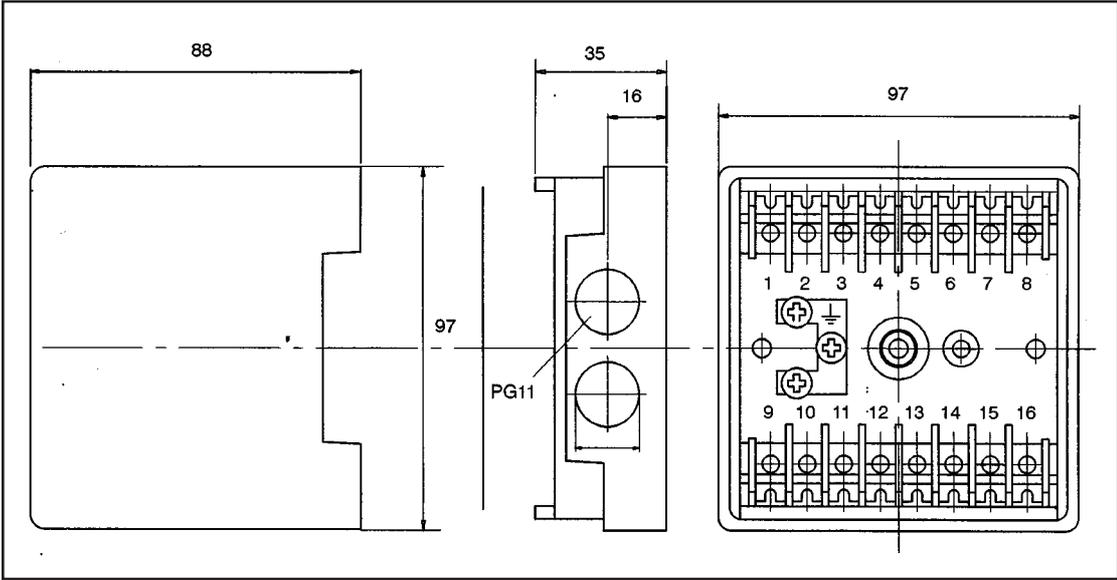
Dimensions du A4021A et de l'embase (en millimètres)
